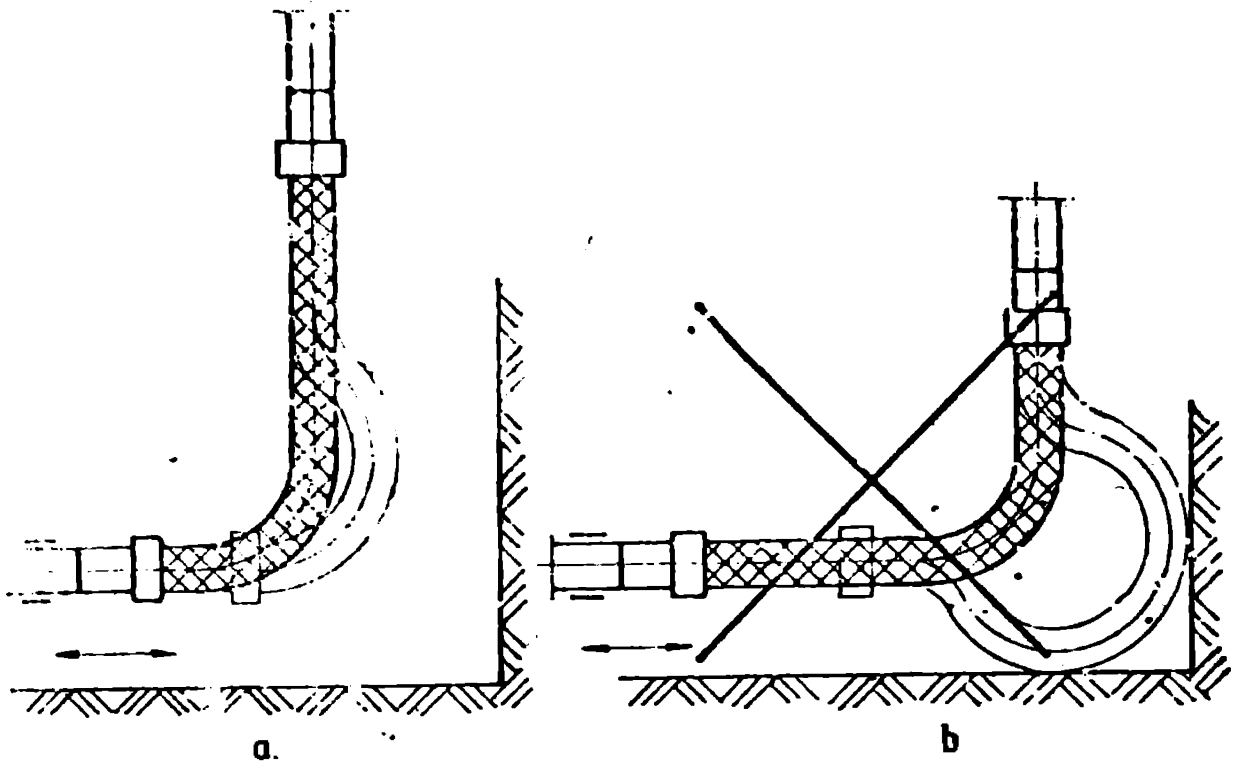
Montaj în arc de 90° cu capătul orizontal mobil.
